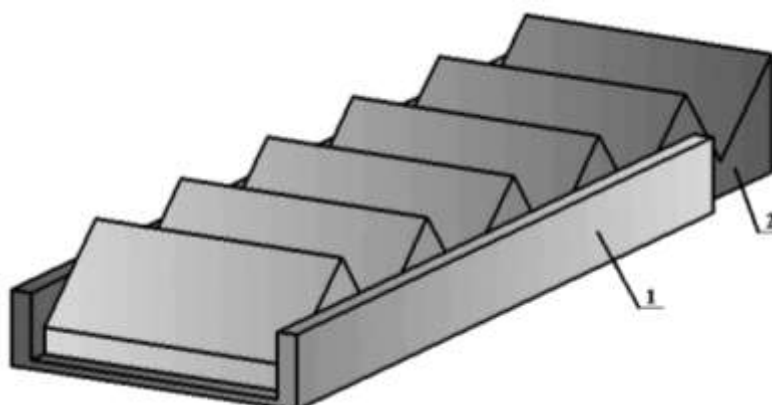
Конструктивная схема рабочего органа со съемной ступенчатой поверхностью:
